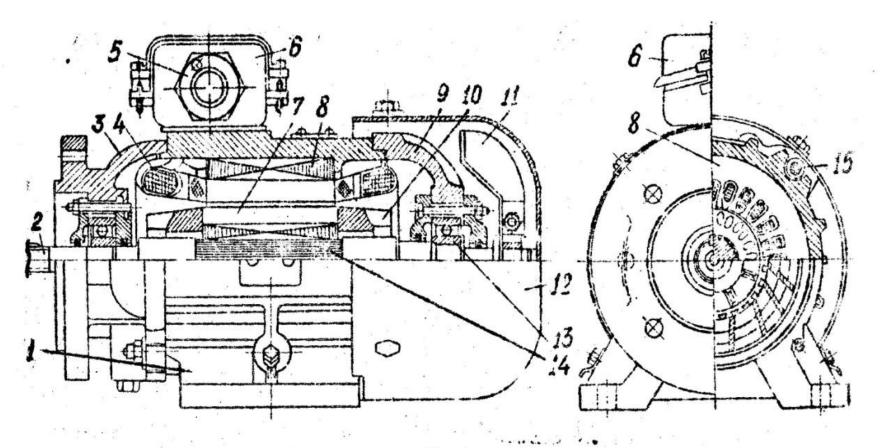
Устройство асинхронного двигателя: I — корпус; 2 — вал; 3 — задний подшипниковый щит; 4 — обмотка статора; 5 — сальник для ввода кабелей; 6 — коробка выводов; 7 — обмотка ротора; 8 — сердечник статора; 9 — передний подшипниковый щит; 10 — вентиляционные лопатки; 11 — вентилятор; 12 — кожух; 13 — подшипник; 14 — сердечник ротора; 15 — шилька
